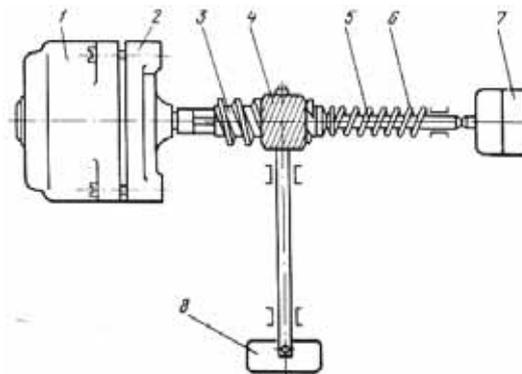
Электромеханический измерительный преобразователь уровня УКМ-Р: 1 – синхронный электродвигатель типа СД-54; 2 – редуктор; 3,4 – червячная пара; 5 – толкатель; 6 – пружина; 7 – микропереключатель; 8 – крыльчатка
